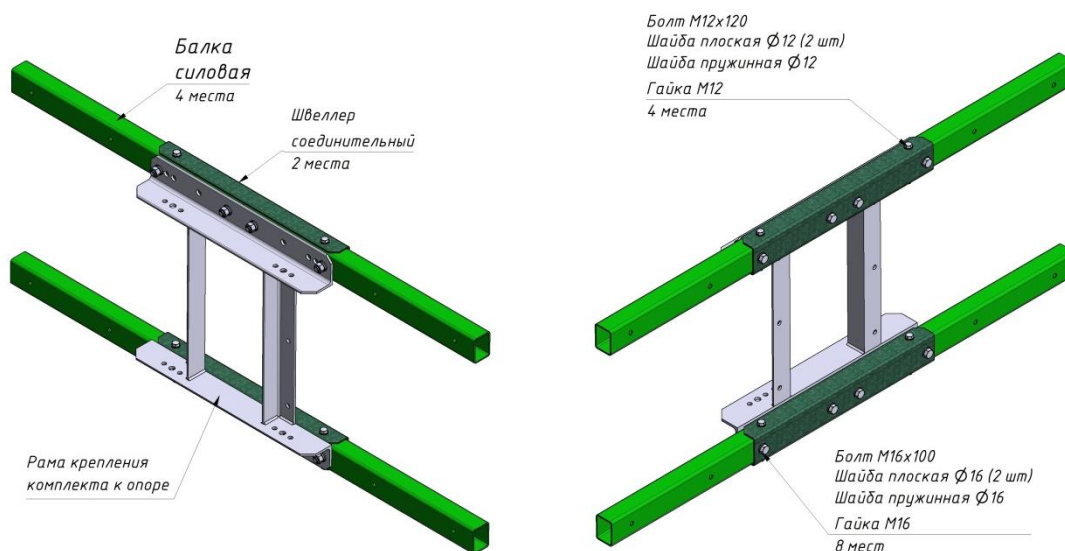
Сборка рамы моноблока для стальных и деревянных опор
